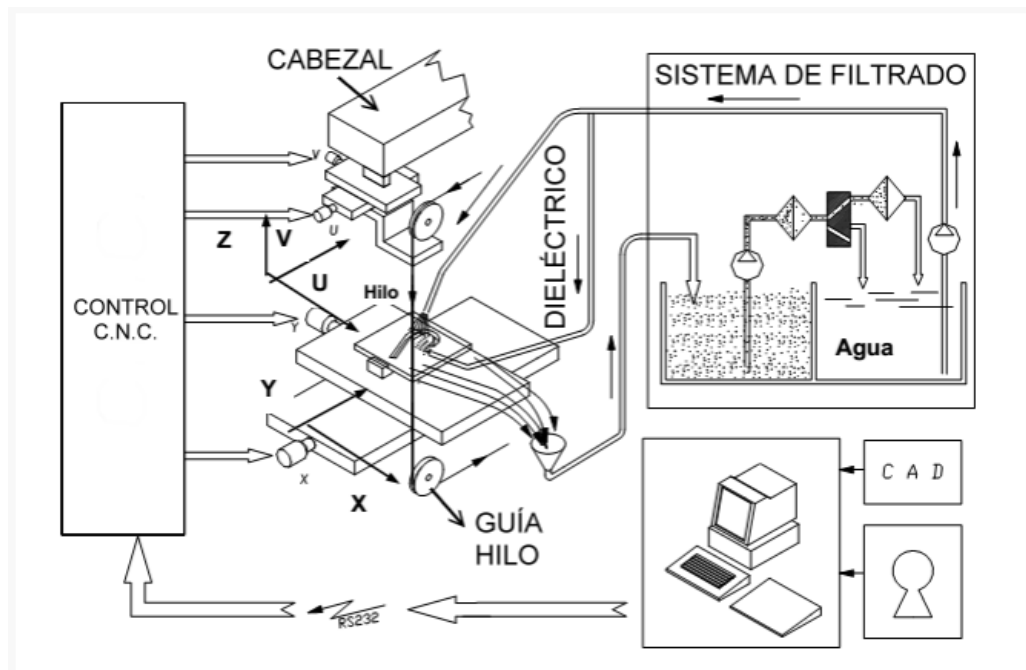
Componentes que integran una máquina electroerosionadora de hilo [17].
